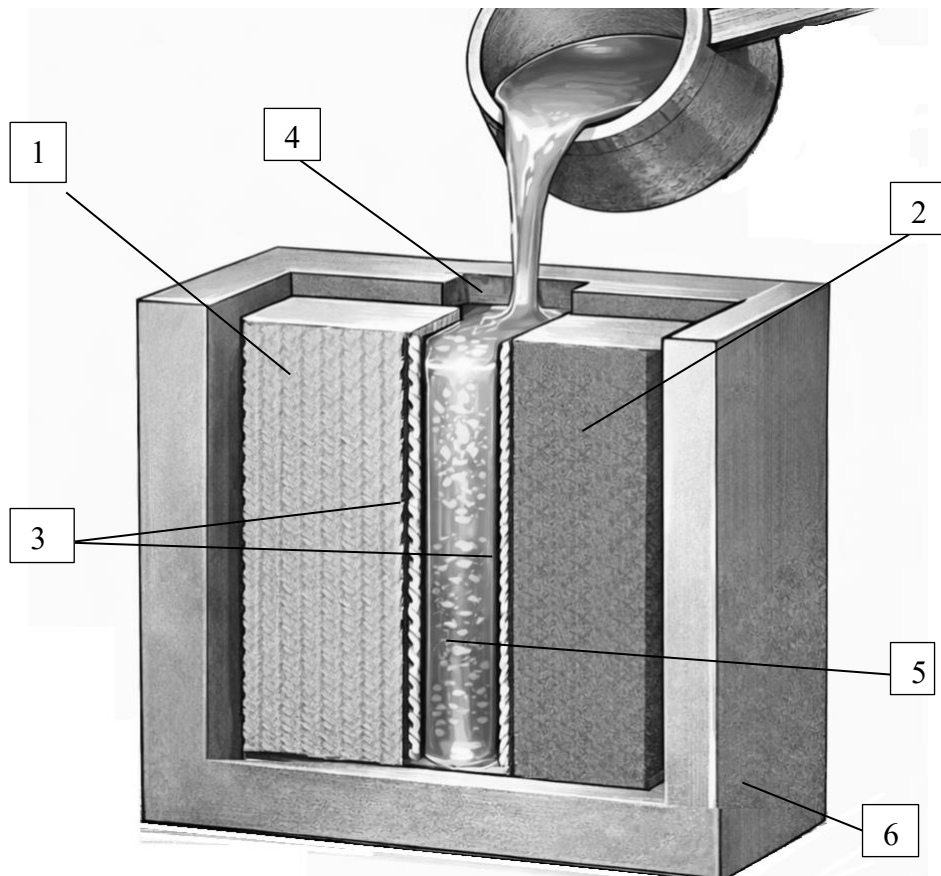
Схема реалізації комбінованого лазерно-ливарного способу формування біметалевого з'єднання з попереднім створенням регулярного макрорельєфу на контактних поверхнях: 1 - металевий шар А; 2 - металевий шар В; 3 - регулярний макрорельєф; 4 - канал міжшарового простору; 5 - рідкий проміжний метал, що заливається у міжшаровий зазор; 6 - ливарна форма (корпус прес-форми)
